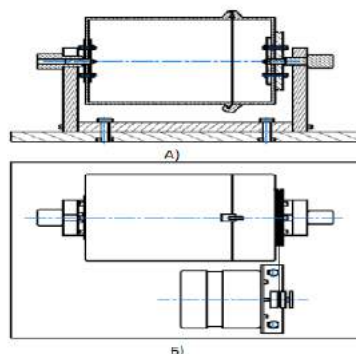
Сборочный чертеж установки по истиранию окатышей. А)-вид сбоку; Б)-вид сверху.
